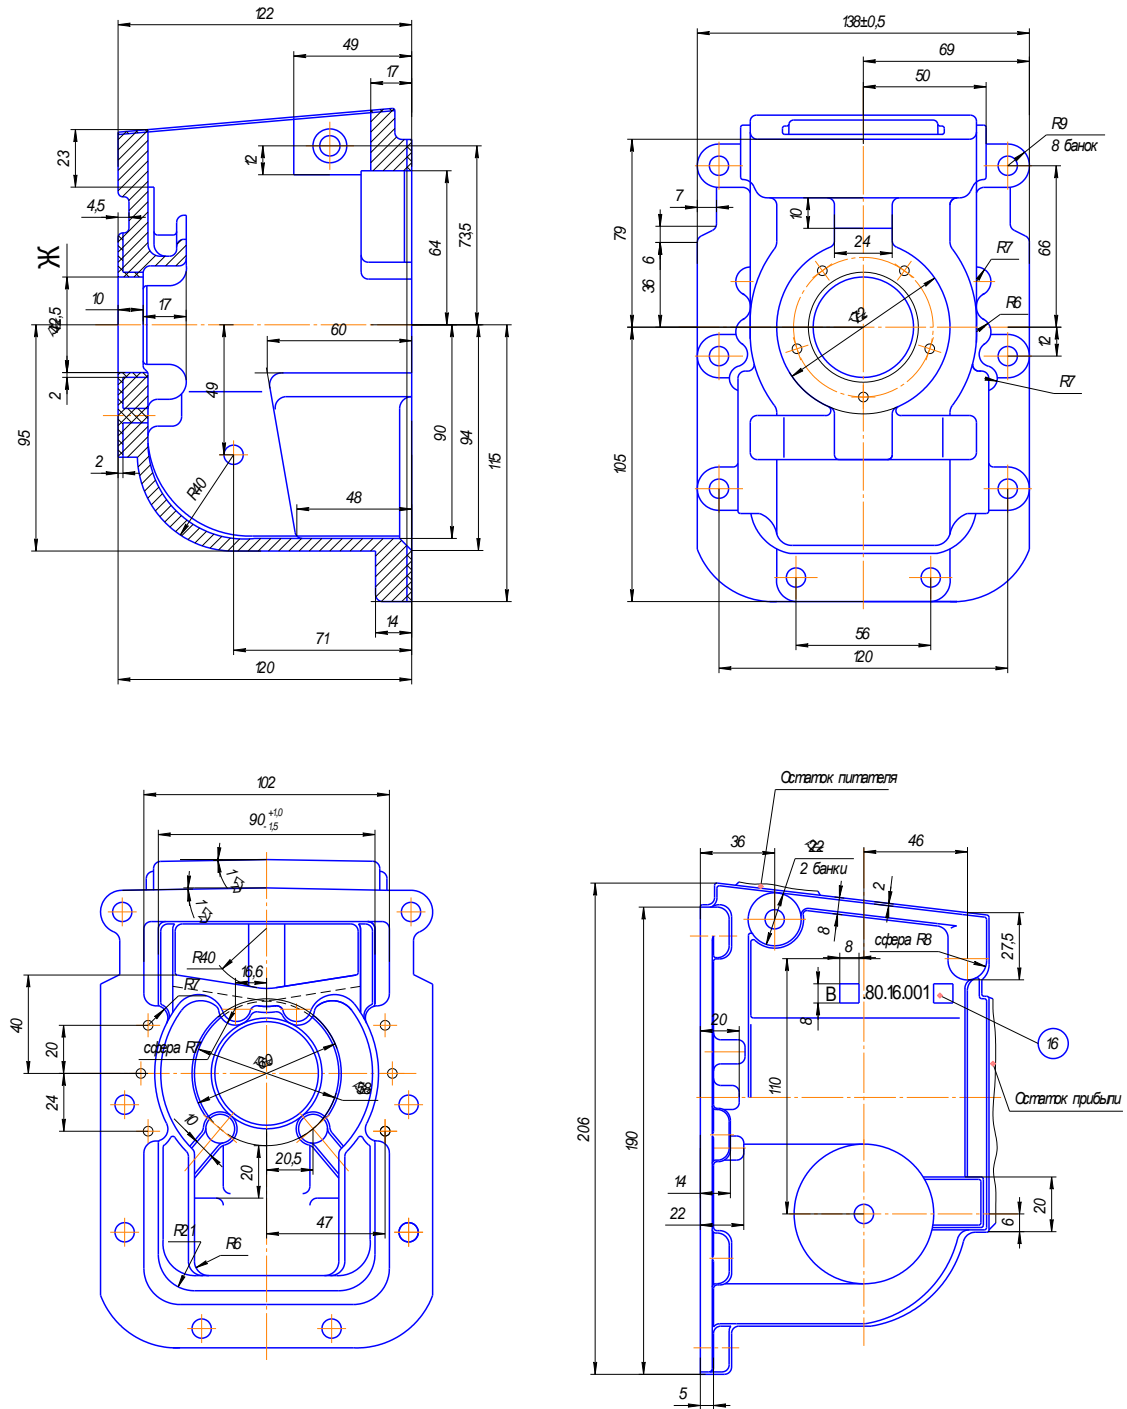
Заготовка корпуса насоса (общий вид)
